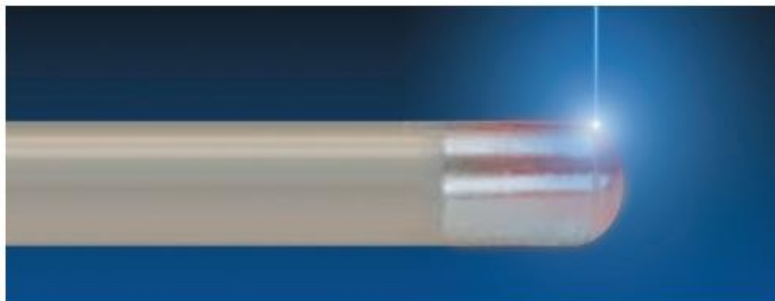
а. Лазерная сварка оболочки первичного преобразователя
